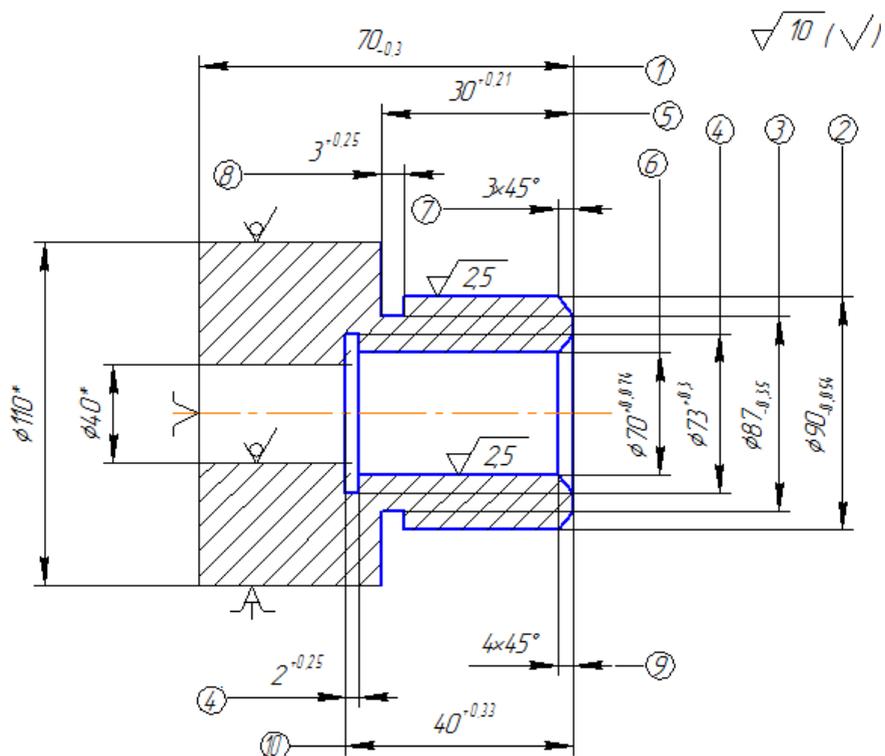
Эскизы заготовки и комплексной операции обработки детали «Кронштейн» на станке модели 2204ВМФ4
